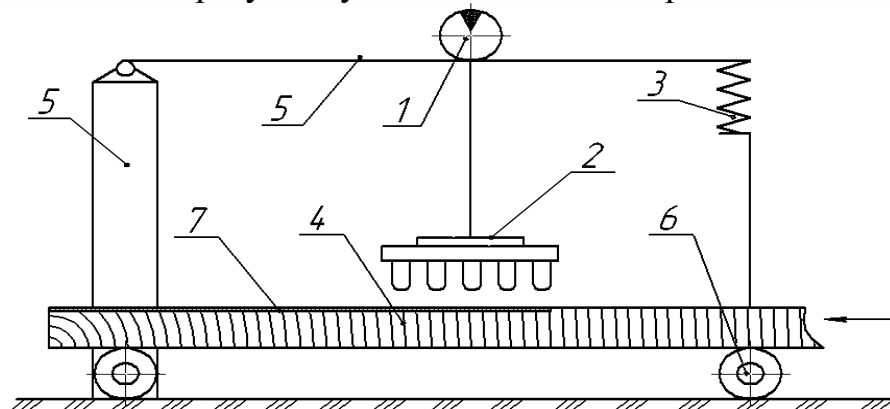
Установка для стационарной обработки поверхностей деревянных конструкций
